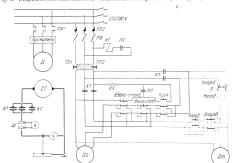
Принципнальная электрическая схема автомата (головки) при сварке на постоянном токе Fig. 6. Diagram of electrical connections of Automatic Welding Machine (welding head) for D.C. welding
